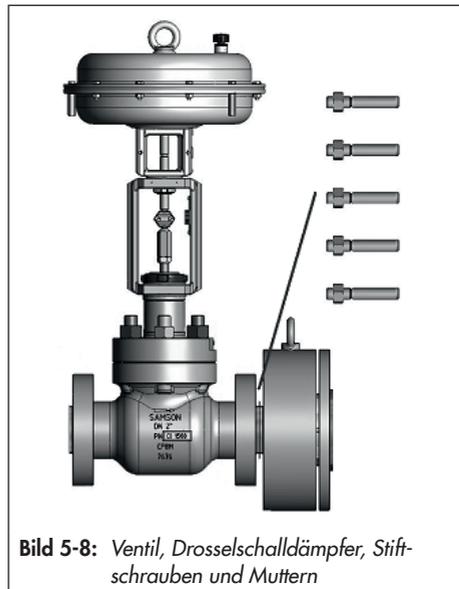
Ventil, Drosselschalldämpfer, Stiftschrauben und Muttern
